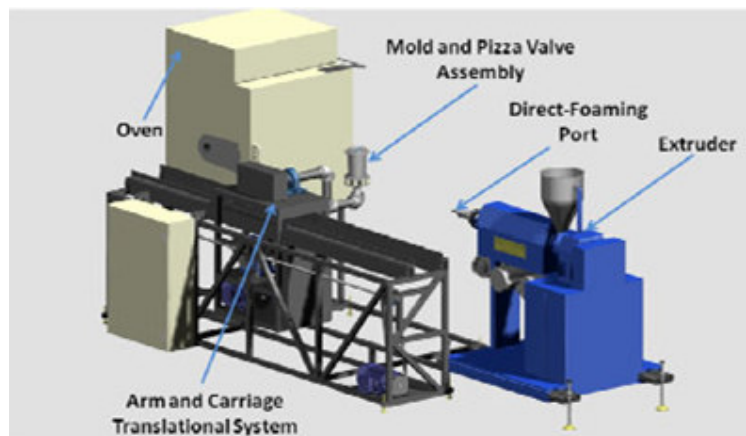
Esquema montaje rotomoldeo con espumado asistido por extrusión.
